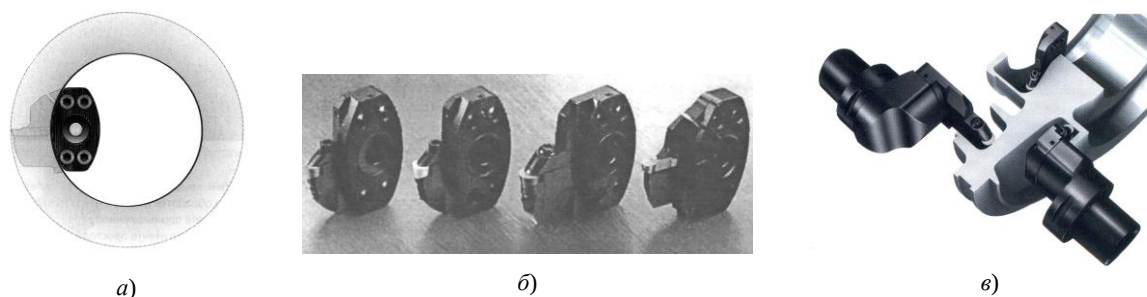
Инструментальная система Coro Turn SL 70: а – схема обработки сложных поверхностей и карманов; б – режущие головки; в – режущие головки с адаптерами
